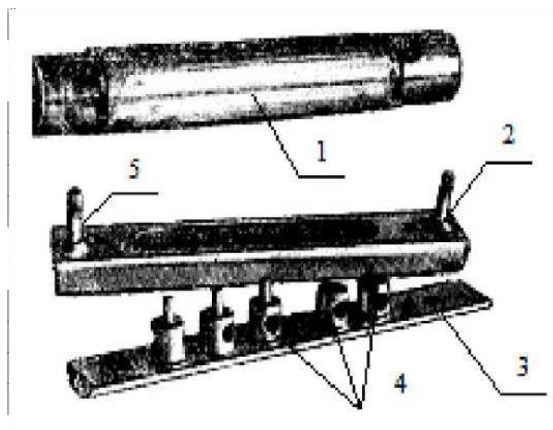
Загальний візуальний вигляд пристрою для вимірювання міцності зчеплення:
